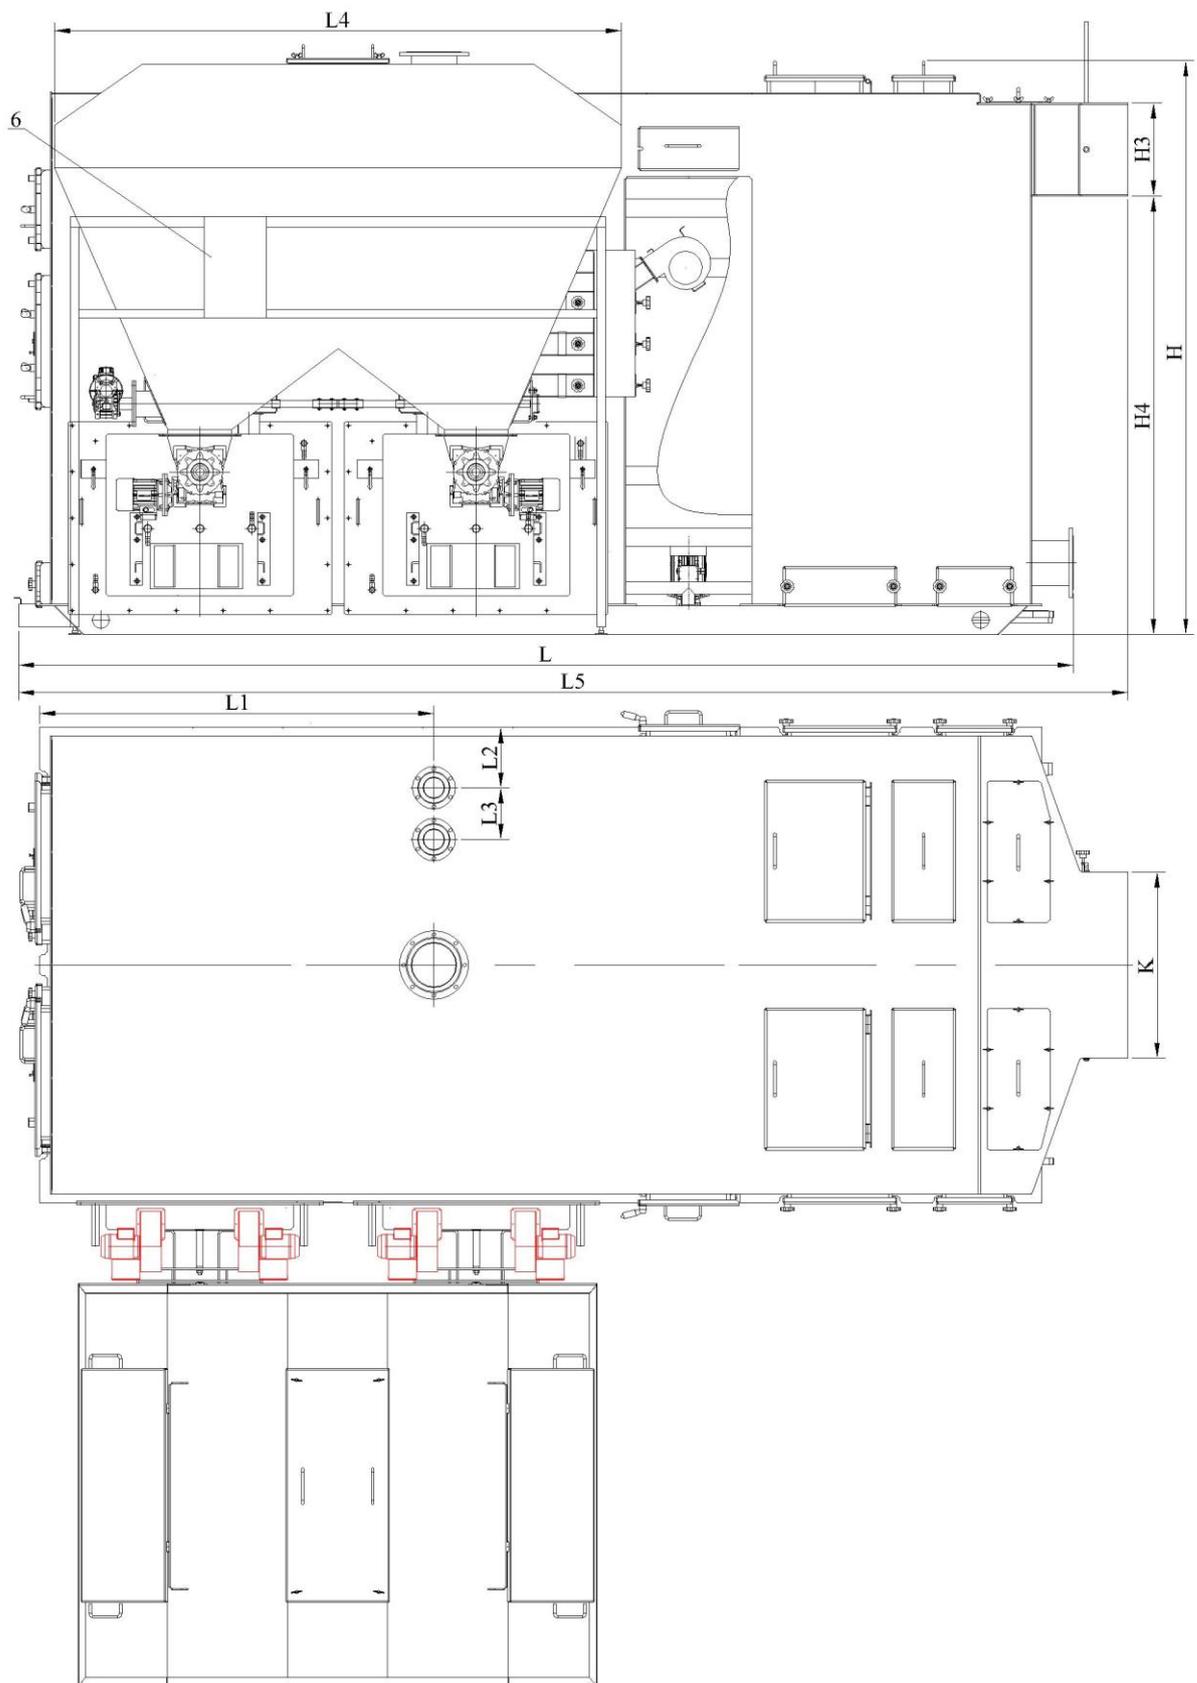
Габаритные и присоединительные размеры котлоагрегата
